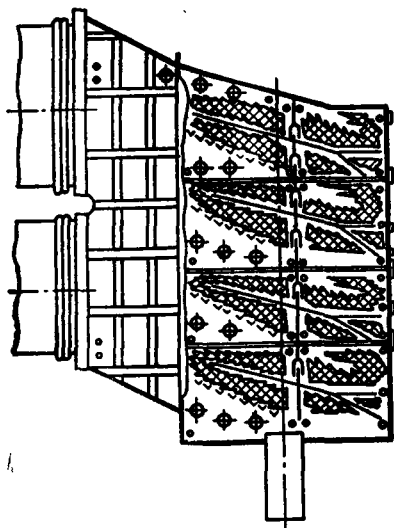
Компоновка трубного пучка бокового конденсатора турбины К-500-60/1500
